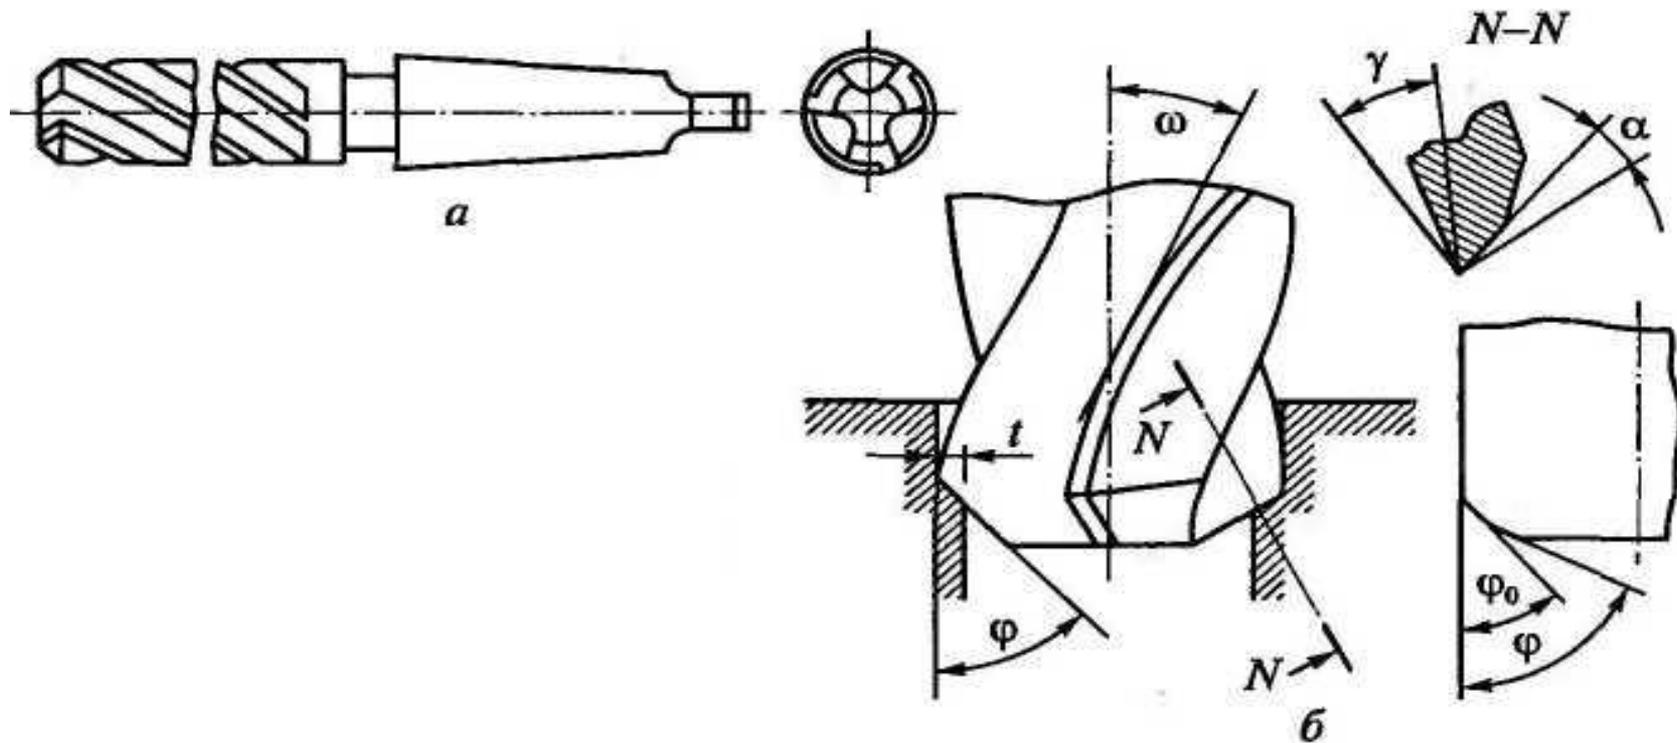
Зенкер: а - конструкция; б - геометрические параметры рабочей части: ω - угол наклона ленточки; φ - главный угол в плане; φ_0 - угол заборного конуса; γ - передний угол; α - задний угол; t - глубина резания
